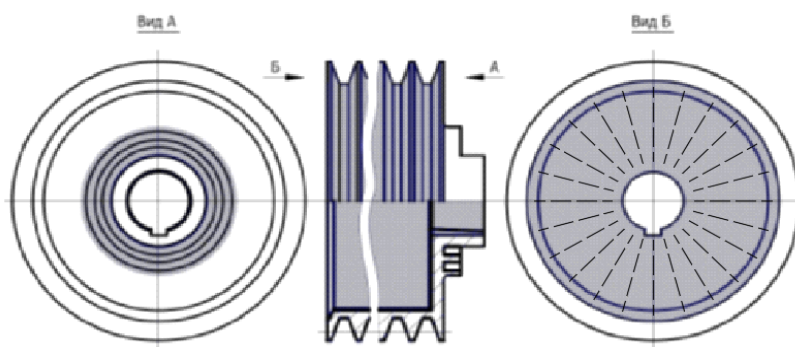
Схема сканирования шкива редукторно-карданного привода
